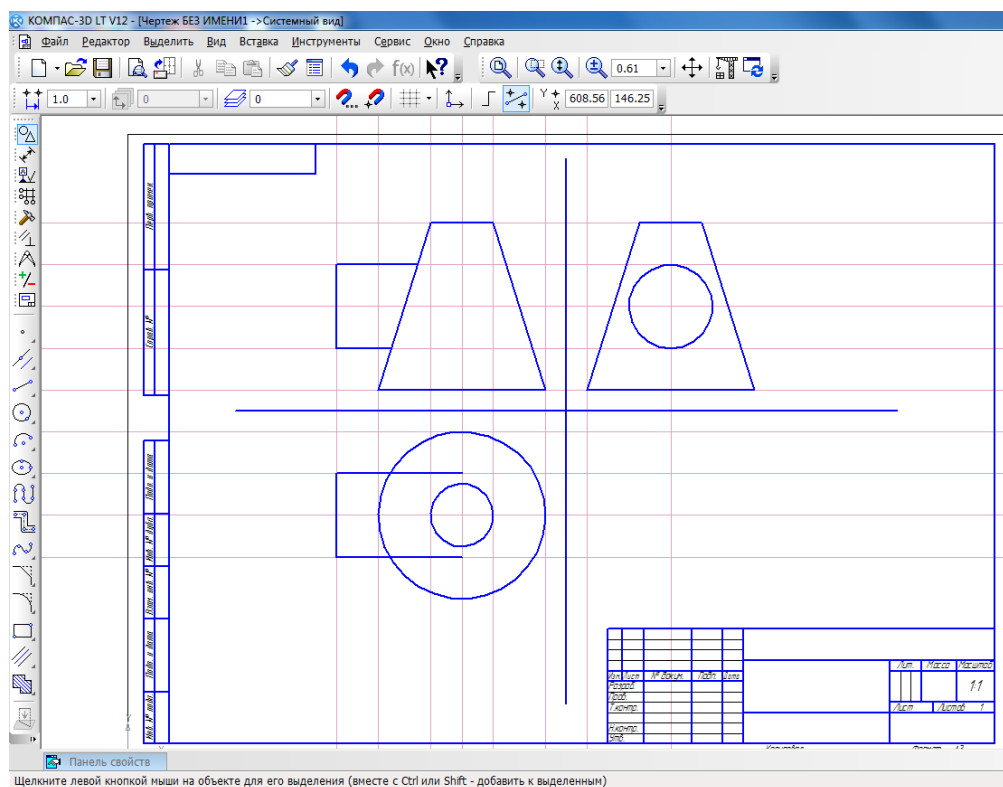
Два пересекающихся тела – усеченный конус и цилиндр
